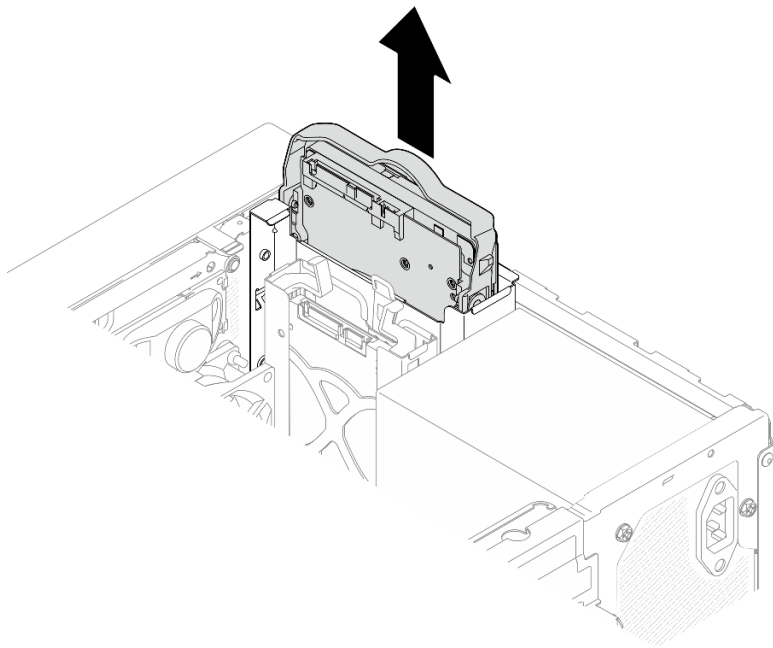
Entfernen einer Laufwerkbaugruppe aus Laufwerkposition 0
